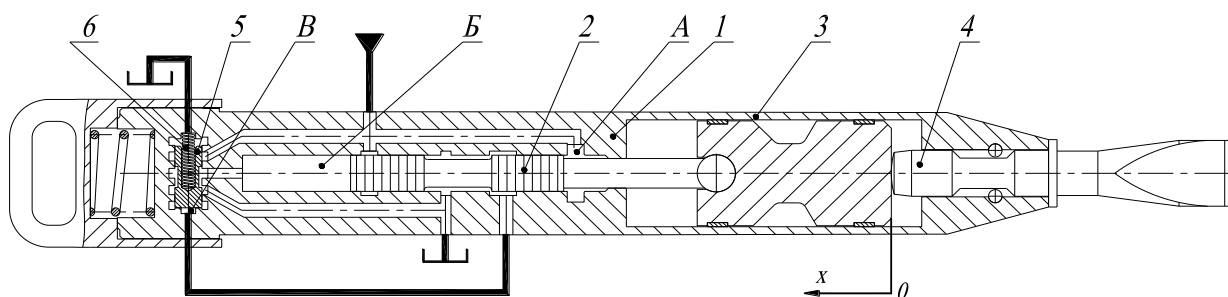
Схема гідромолотка з керованою камерою робочого ходу
